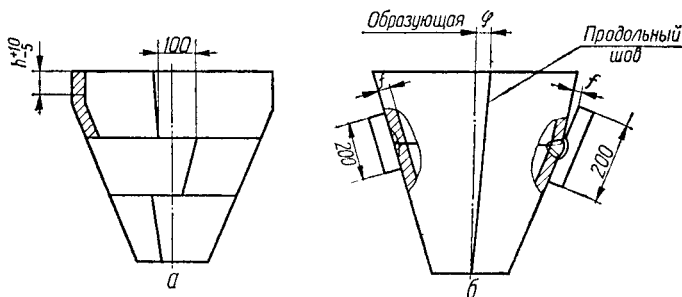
Расположение сварных швов в конических днищах.
